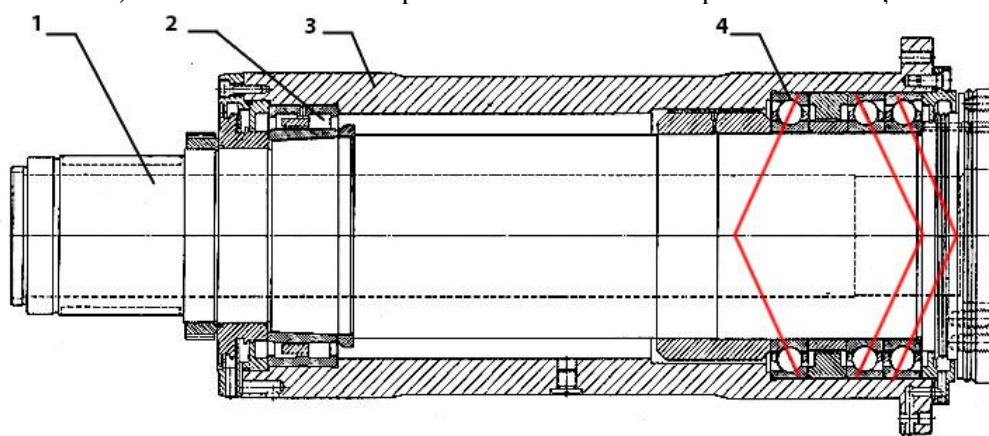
Arbore principal SKF cu transmisie prin curea. 1 – arbore; 2 – rulment radial cu role cilindrice pe două rânduri; 3 – carcasă; 4 – lăgăruire cu rulmenți radial-axiali cu bile, montaj în “O”.
